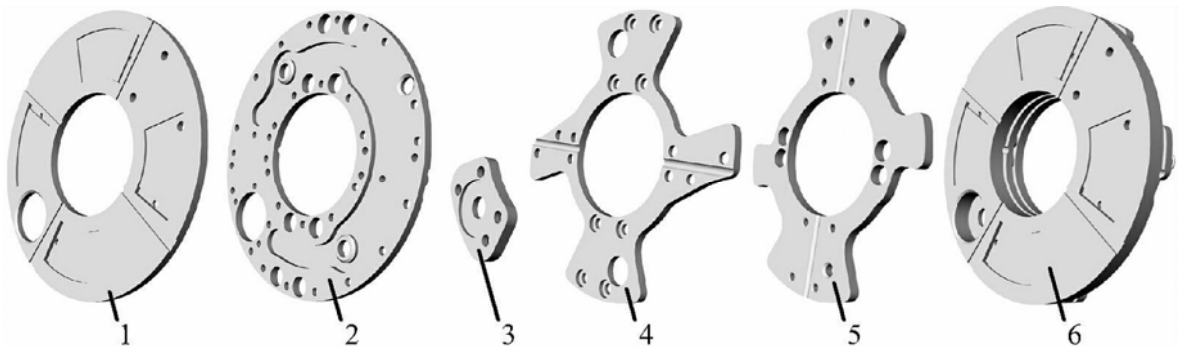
Основные детали и общий вид опытного образца гидростатодинамического подпятника с карманами Рэлея: 1 – верхний диск; 2 – нижний диск; 3 – крышка токовихревого датчика; 4 – верхняя крестовина; 5 – нижняя крестовина; 6 – опытный образец в сборе
